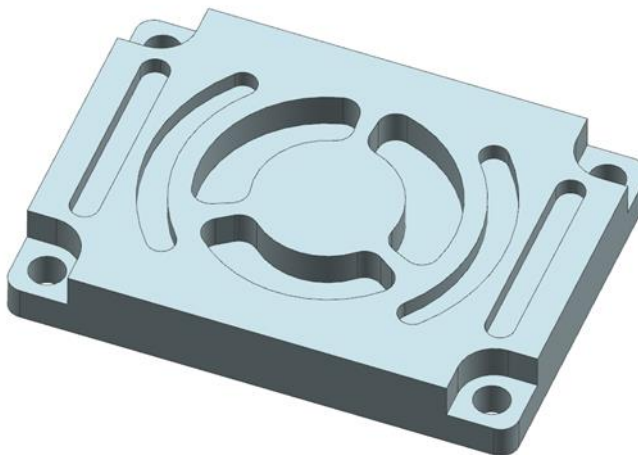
Параметрическая 3D модель детали типа «Плита»
